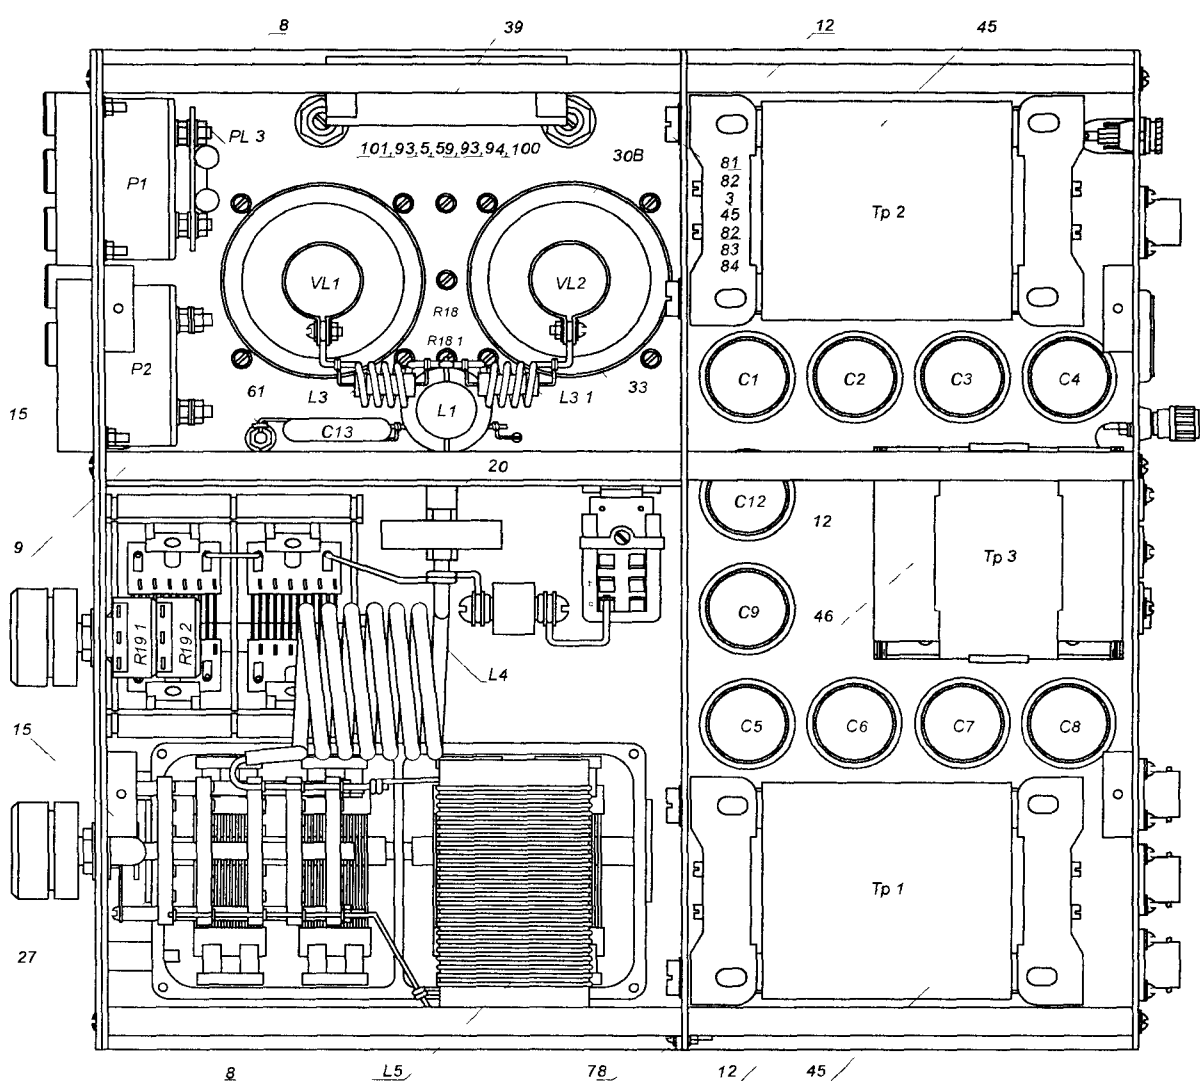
В. Сборочный чертеж усилителя DVA-300B Вид сверху со снятой верхней крышкой
